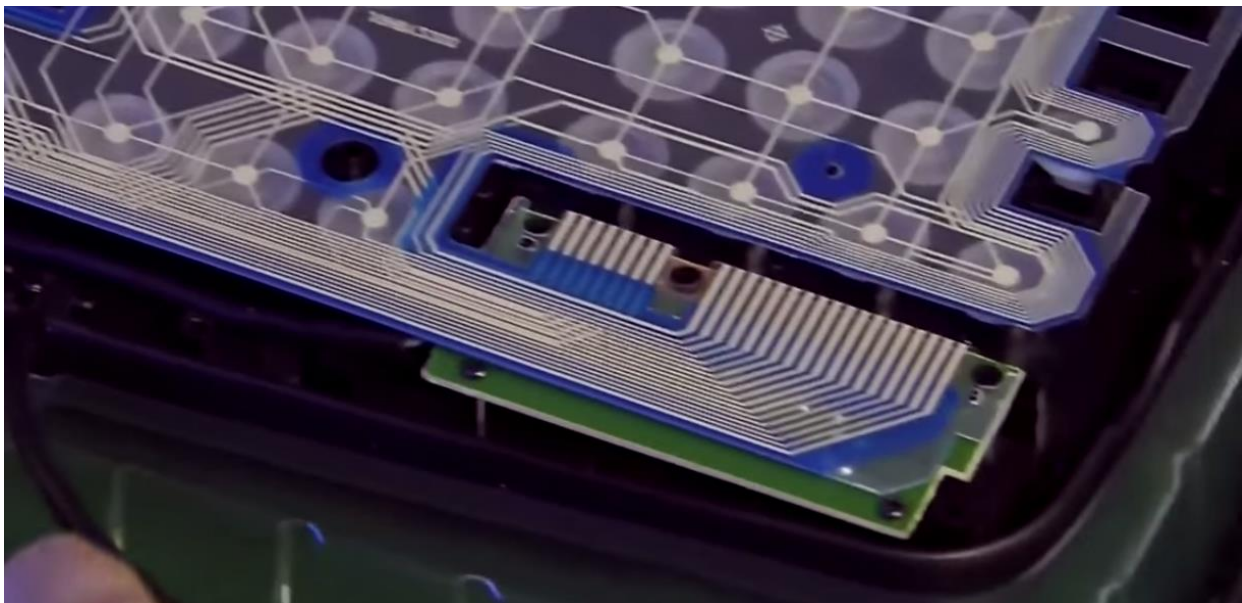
Установка готовой платы и мембраны в корпус клавиатуры
